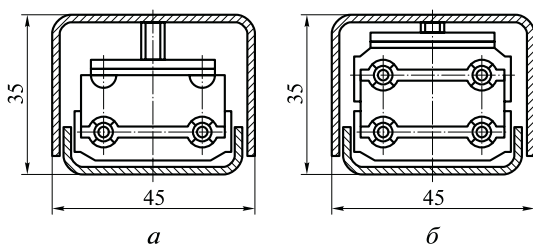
Поперечное сечение осветительного шинопровода ШОС:
